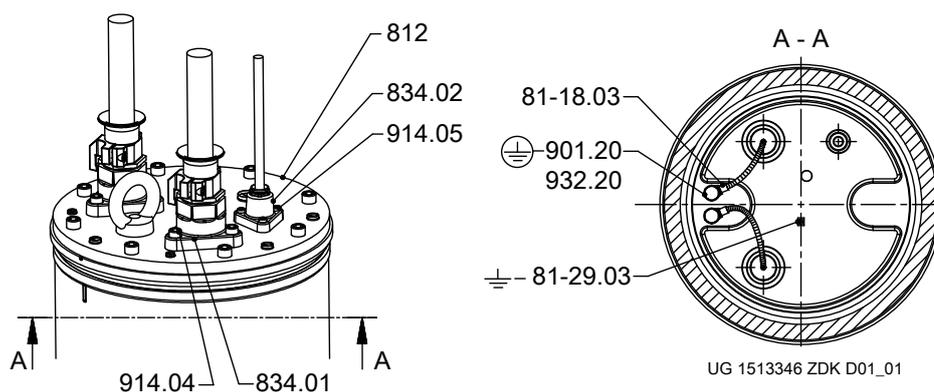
Desmontaje del paso de cables y del cable de conexión
